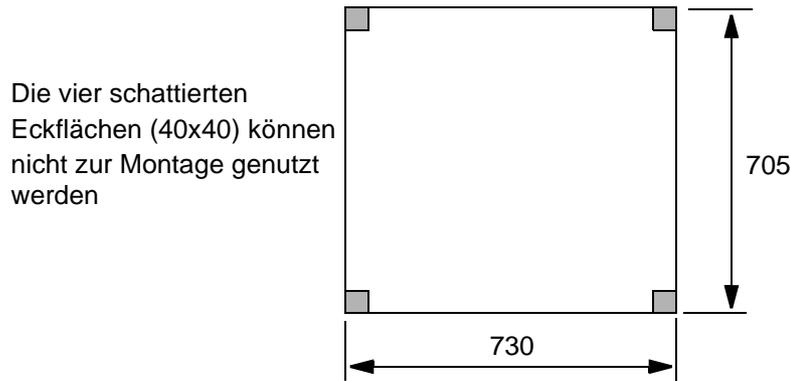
Montageblech zur Befestigung von Geräten (Abmessungen in mm)
